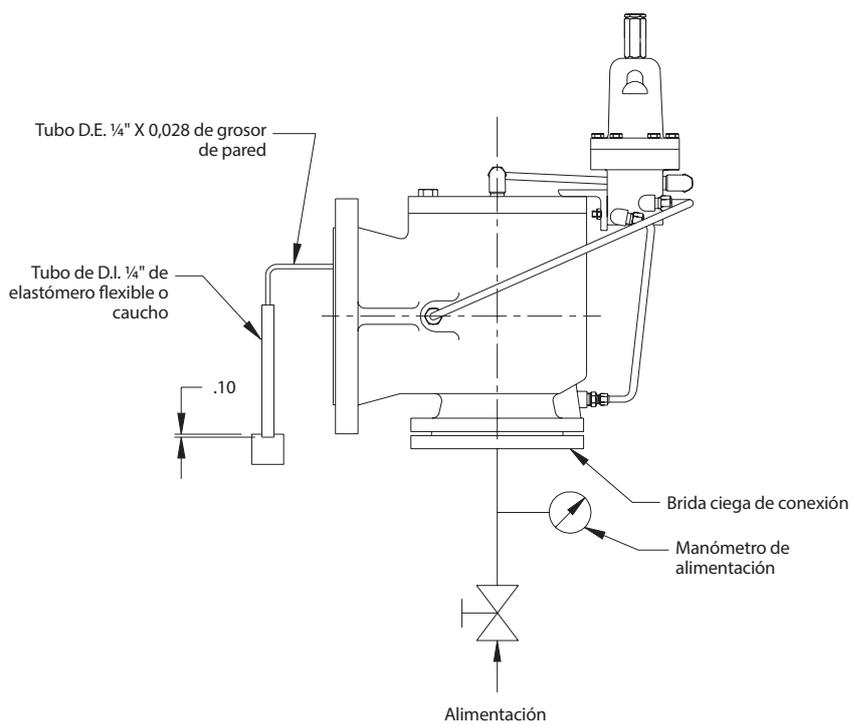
MONTAJE DE ENSAYO PARA VÁLVULA CON PILOTO ESTÁNDAR
